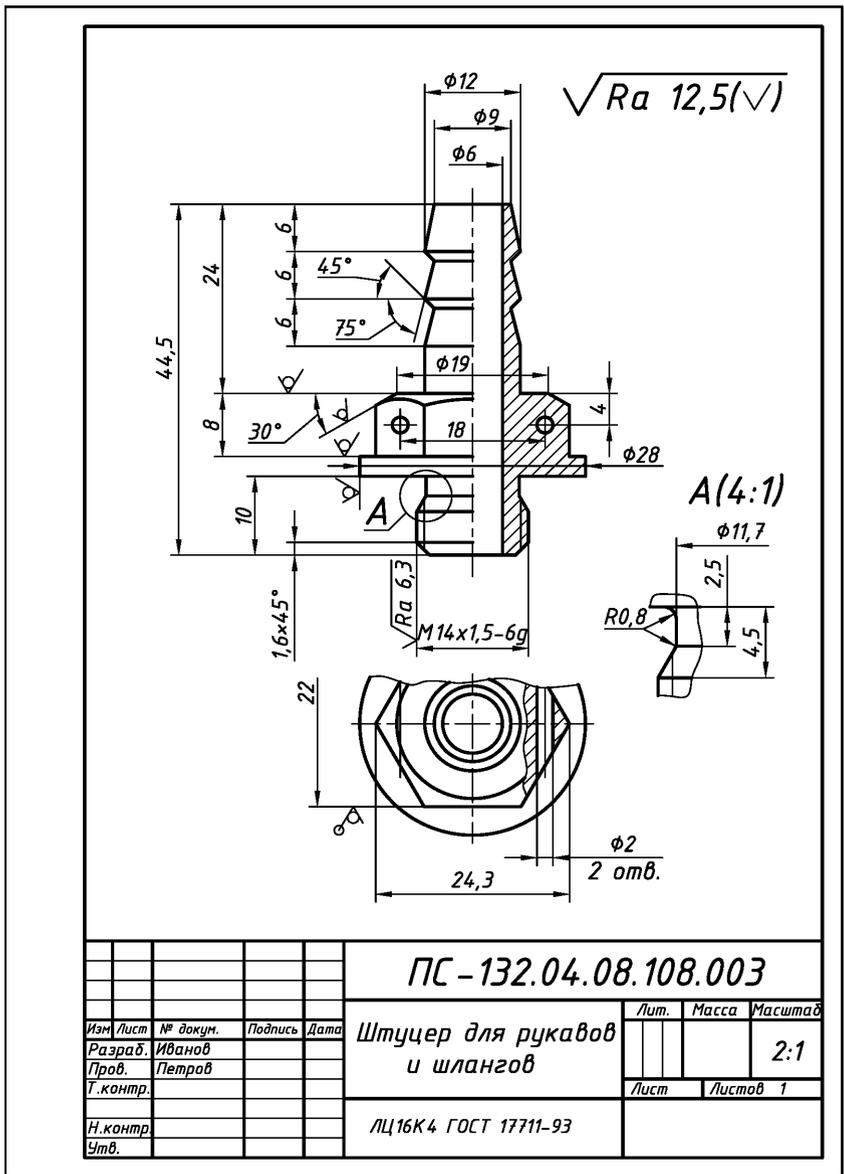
Оформление рабочего чертежа литой детали из металла с обработкой
